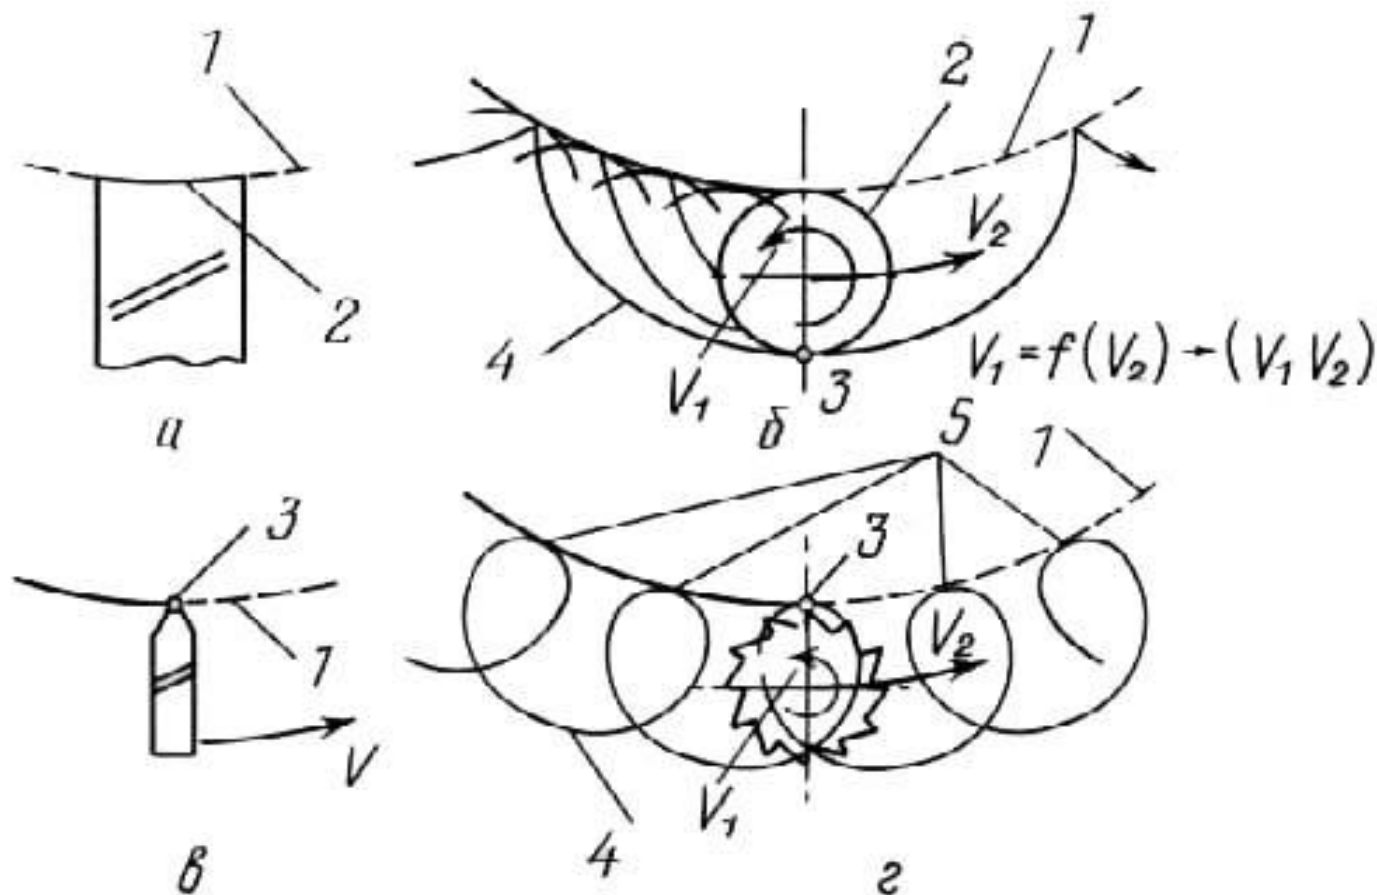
Схемы методов формообразования производящих линий: 1 – образуемая производящая линия; 2 – режущее лезвие инструмента; 3 – режущая кромка инструмента; 4 – траектория движения режущей кромки 3 инструмента; 5 – точки касания режущей кромки 3 инструмента производящей линии 1; V_1, V_2 – относительные скорости
